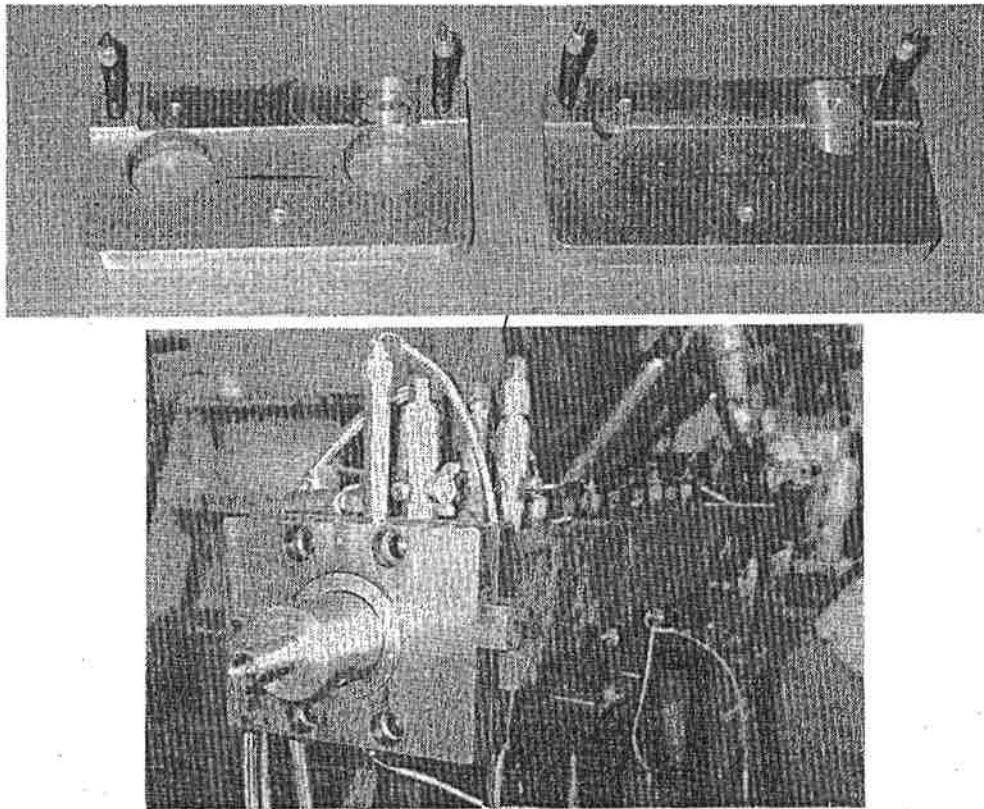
Barrel Heater 및 Heater 장착 barrel의 조합후 전경
